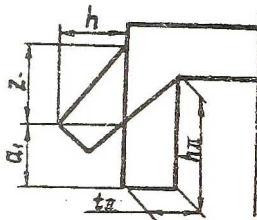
Схема свертки профиля в предчистовом калибре
